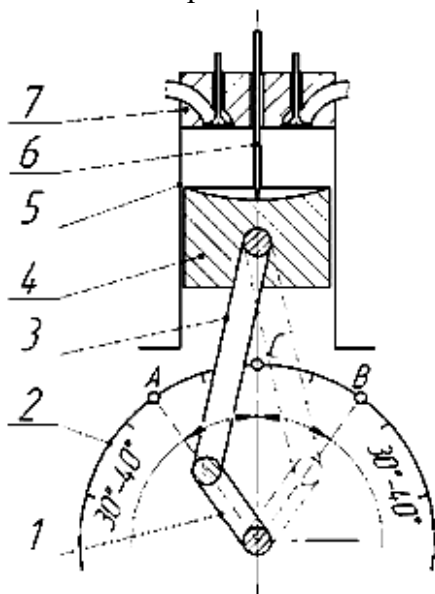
Определение мертвых точек 1 - Коленчатый вал; 2 - Маховик; 3 - Шатун; 4 - Поршень; 5 - Цилиндр; 6 - Металлический стержень; 7 - Крышка цилиндра
